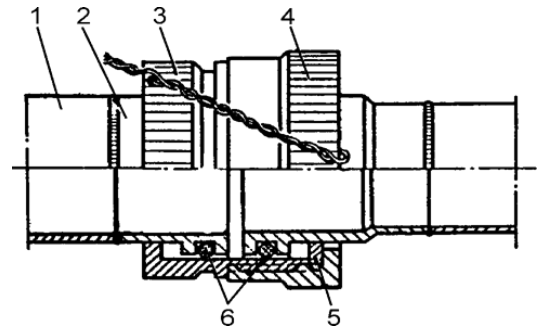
Обмежено-рухливе з'єднання трубопроводів:
